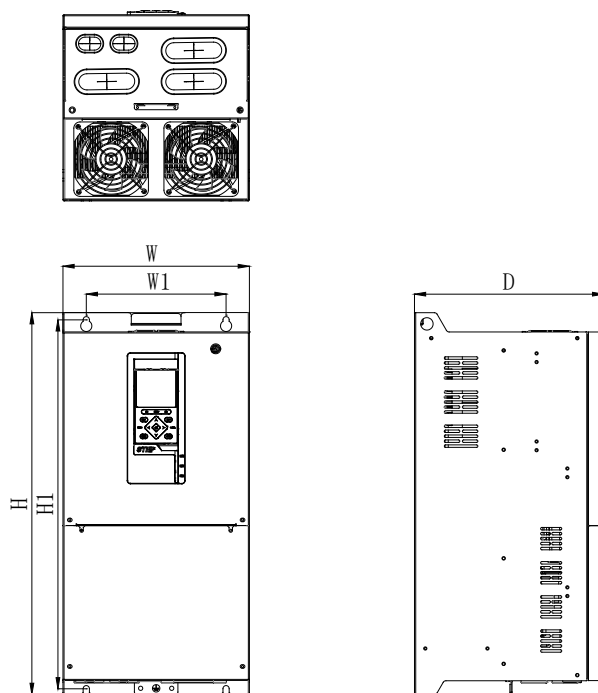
Установочные размеры инверторов F6 - F8
